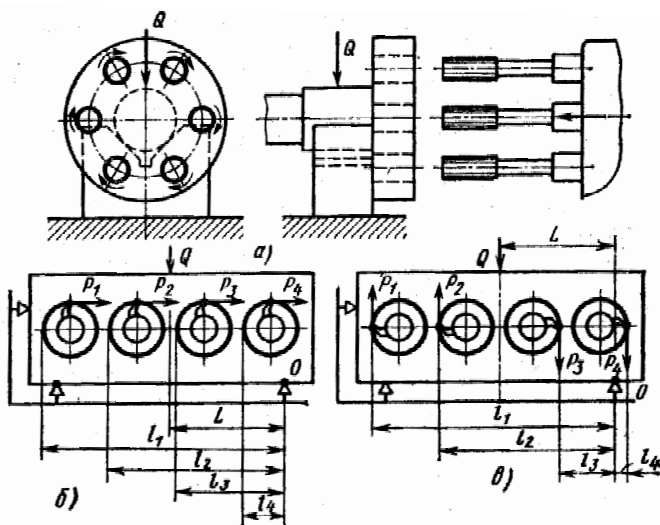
Схемы для расчета сил закрепления заготовок при многоинструментной обработке
